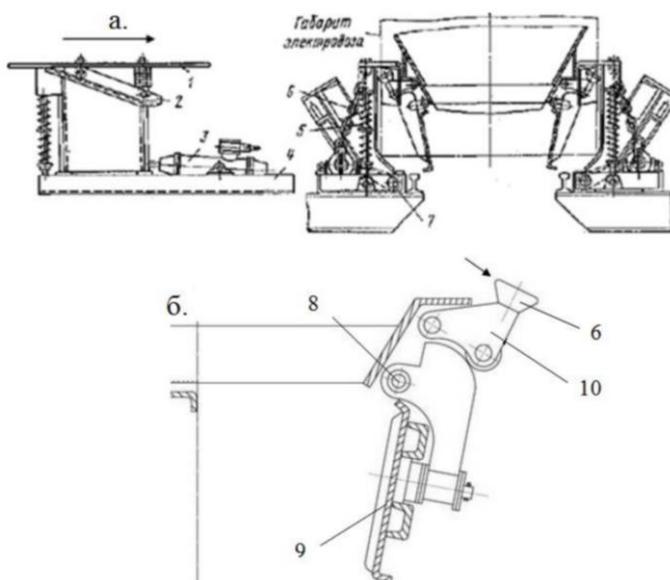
Устройство для закрывания днищ (клапанов): а – общий вид, б – положение роликового замкового устройства при открытом днище.
